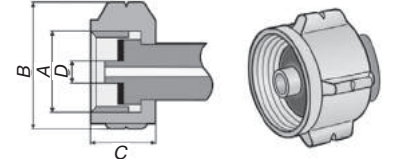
ГОСТ 6357-81 «Резьба трубная цилиндрическая», основные размеры:
